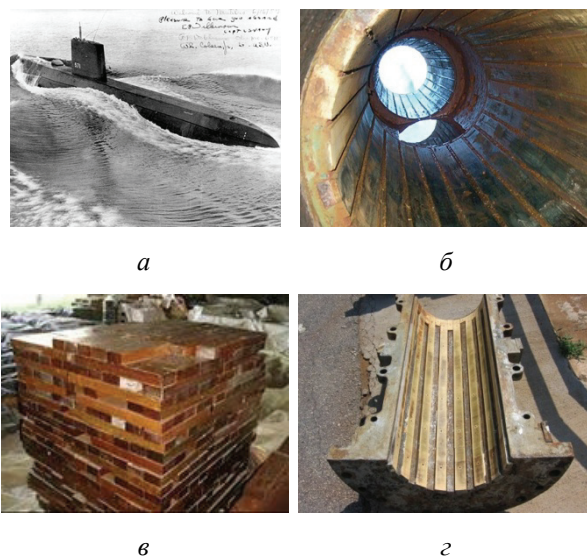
Подлодка (а), подшипник гребного вала (б), заготовки для набора подшипника (в), полувкладыш (г)
